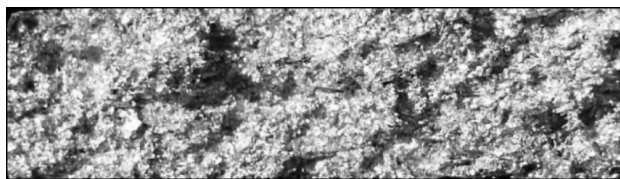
Внешний вид поверхности излома образца коркового алюминиевого напыления (×10)
